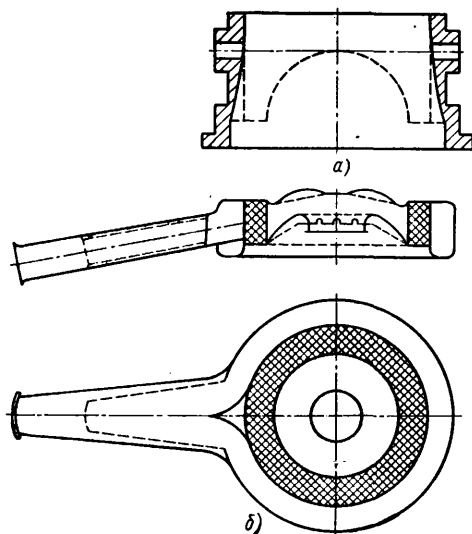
Крышка карбюратора (а) и воздушный фильтр двигателя (б)
